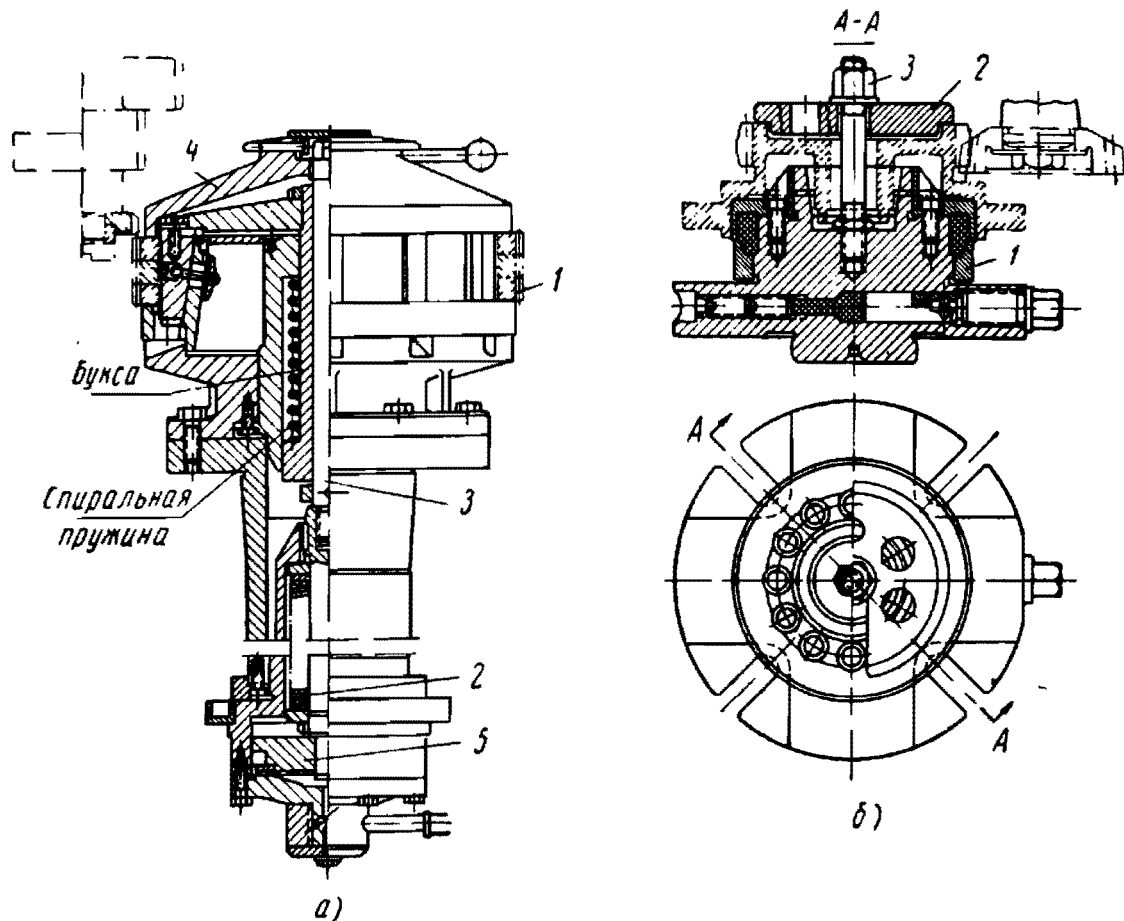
Приспособления для установки и закрепления нарезаемых колес на зубодолбежном станке
